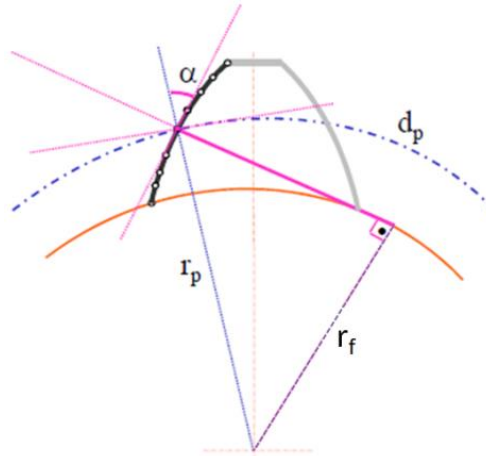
Perfil de dente de engrenagem. (Fonte: Grupo de Projeto. Aula 2 - Transmissões por Engrenagens)
